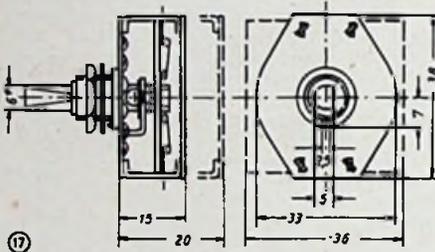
Löffelschalter E 9. Abb. 16. Trimmerplatte aus Frequenta mit 3 Glimmer-Trimmern. Abb. 17. Maßskizze des Wellenschalters Nr. 951 der NSF mit 1 bis 3 Schaltscheiben
